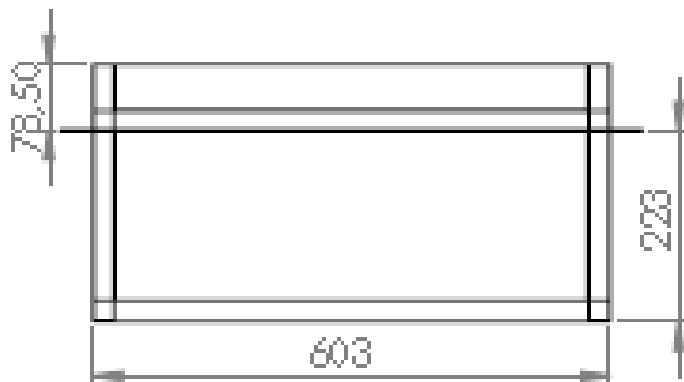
Perfil quadrado de 10 x 10 x 1,2 mm
